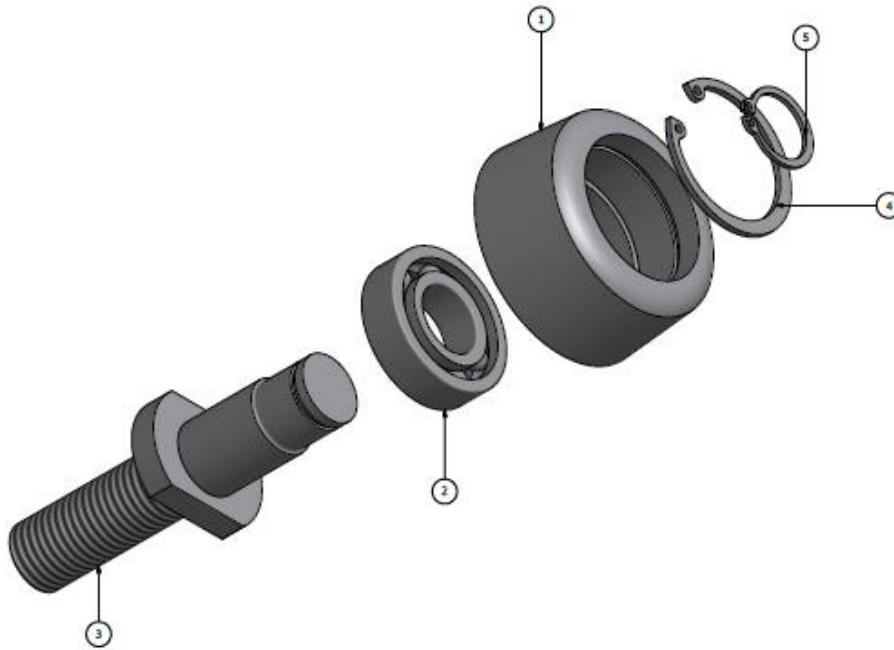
Despiece del Ensamblaje de la Rueda Guía
